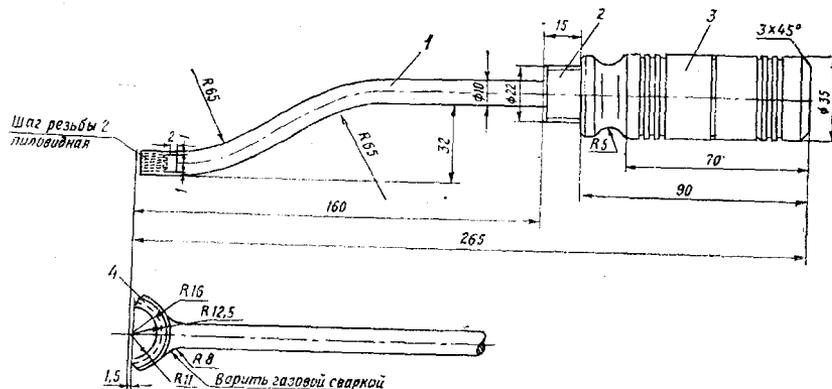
Приспособление для очистки штоков клапанов выпуска:
